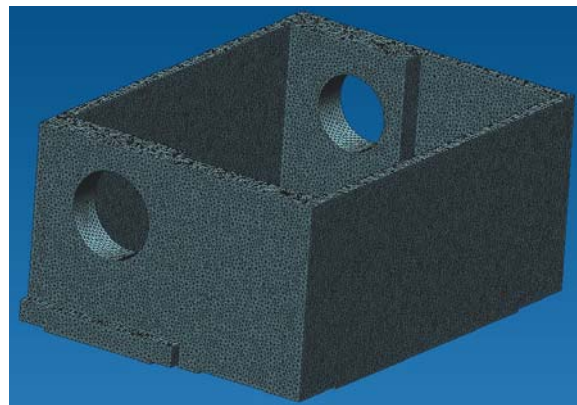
Твердотільна модель корпусу шпинделя розбитого МКЕ
